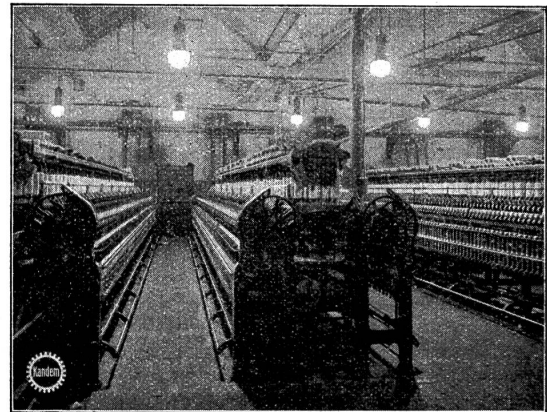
Gut beleuchteter Ringspinnmaschinenraum mit Leuchten für vorwiegend direktes Licht.
